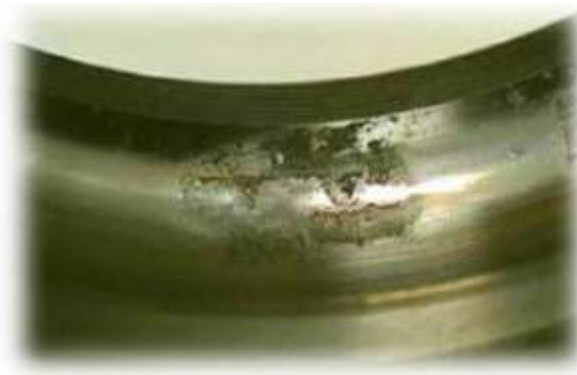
Défaut de roulement – Corrosion.
